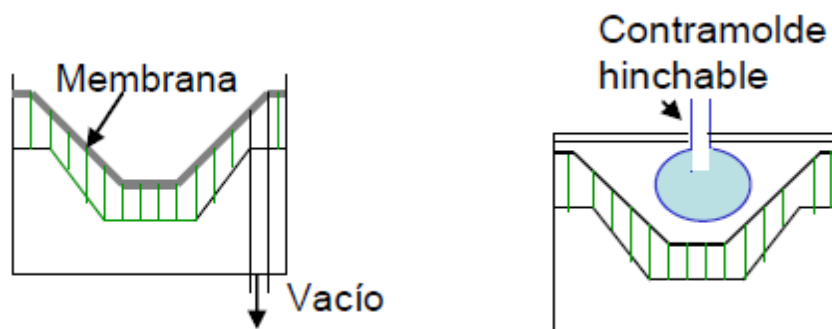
Moldeo al vacío (izquierda) y por presión (derecha).
